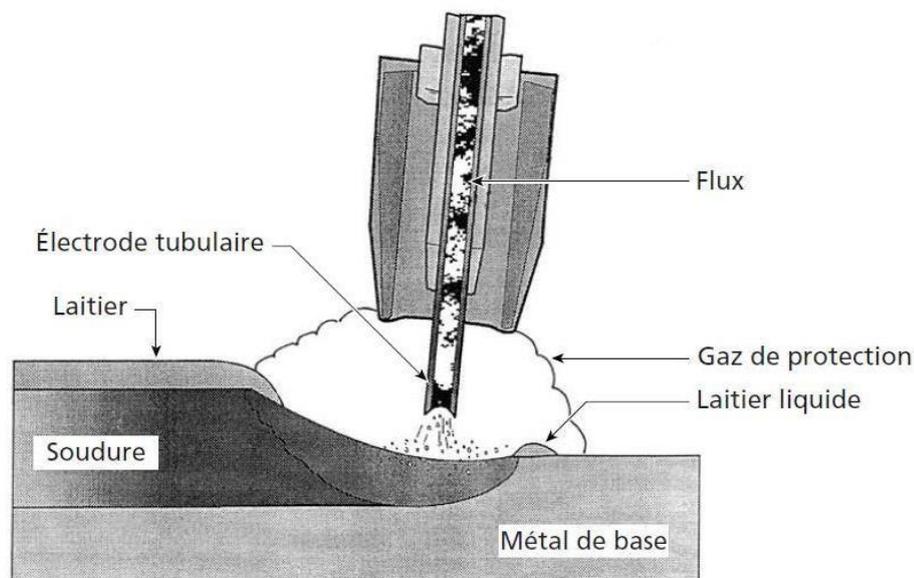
Soudage avec fil fourré et gaz de protection [3].
